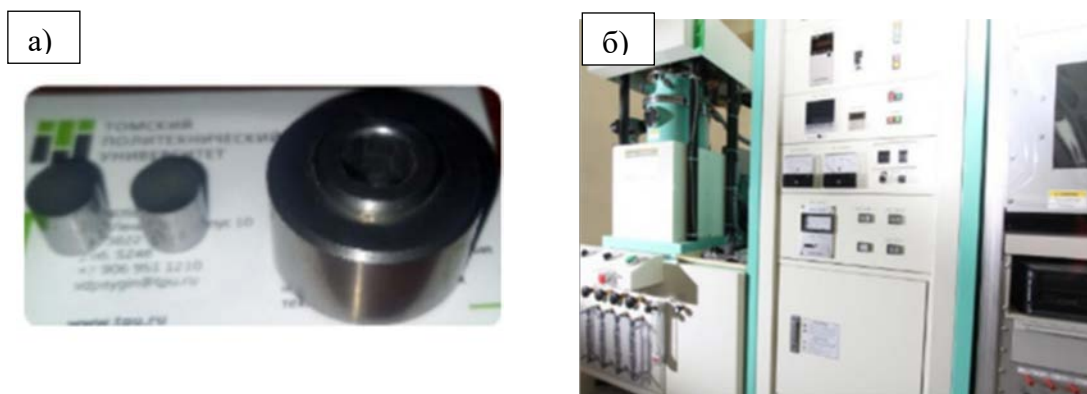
а-Пресс-формы из твердого сплава, б-ЭИПС-515S
